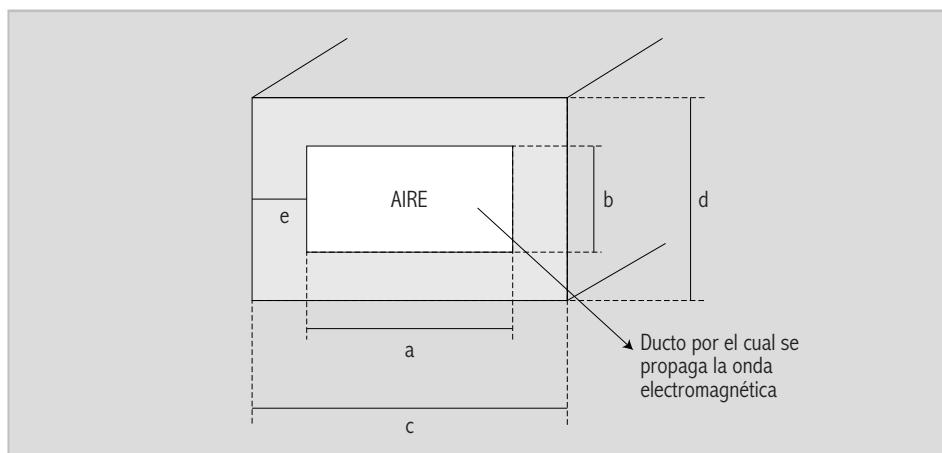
Perfil transversal de una guía de onda rectangular.
